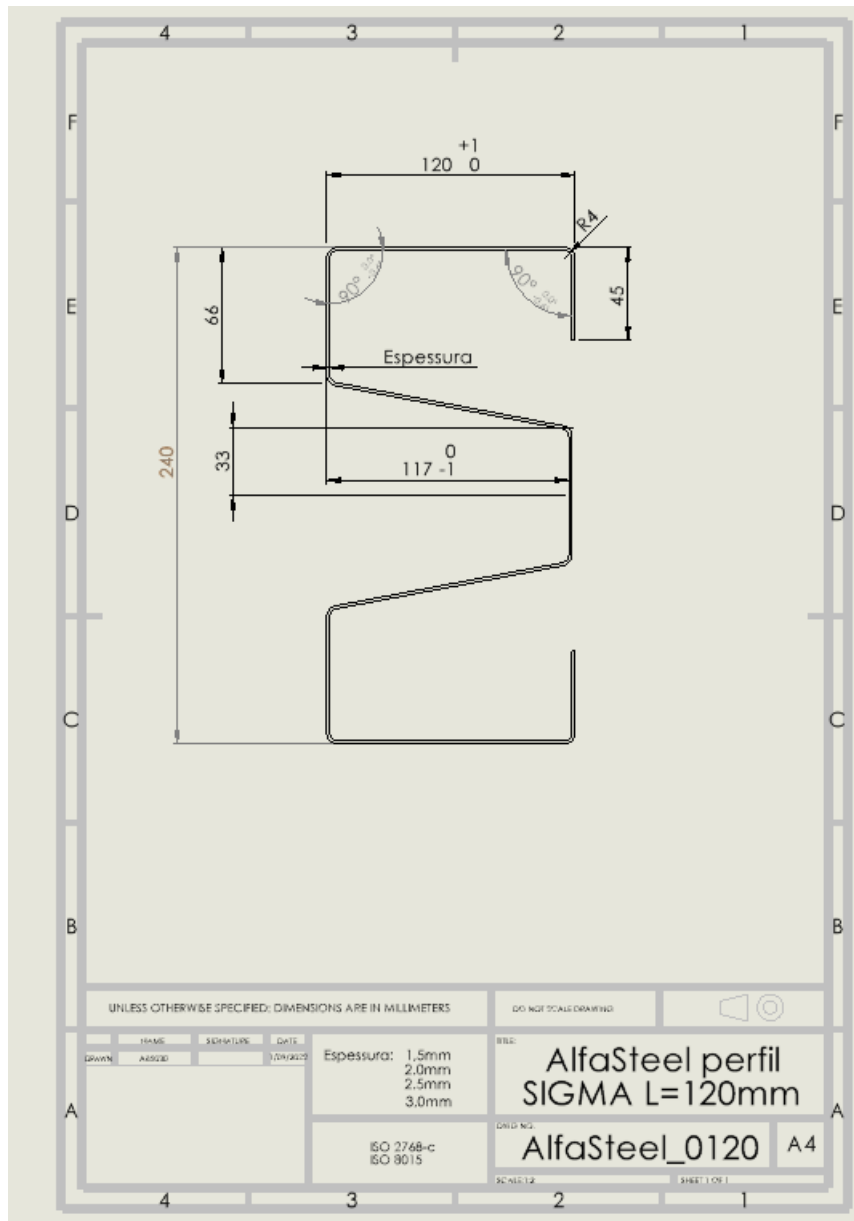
Desenho técnico do perfil de Largura = 120 mm
